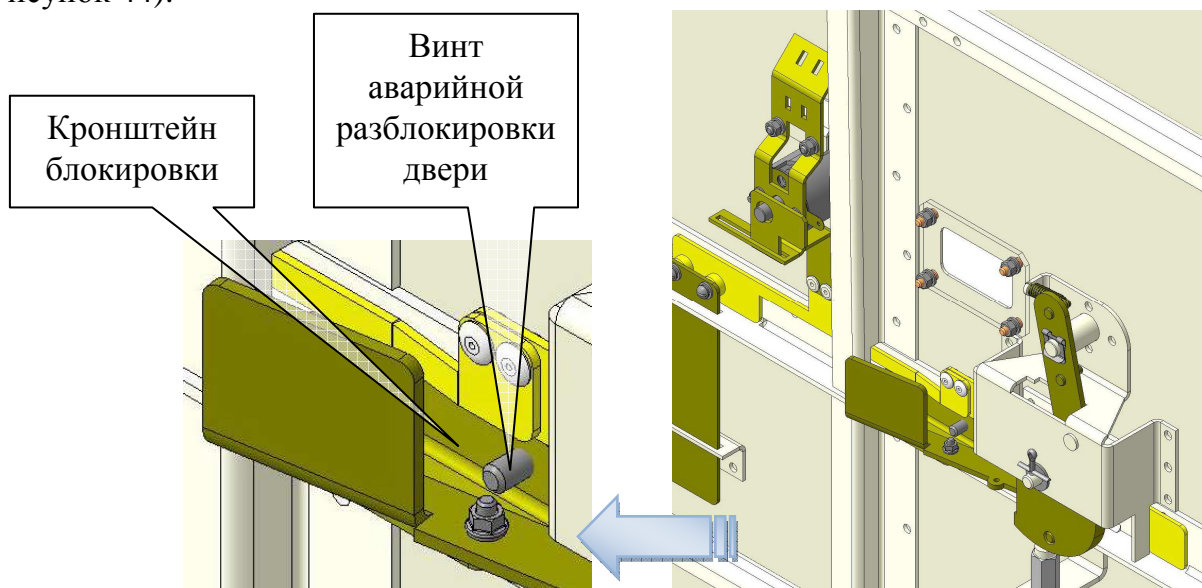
Установка блокировки на двери отсека ВЭ
